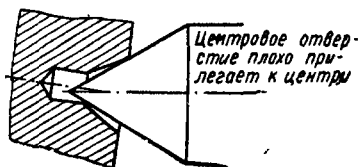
Схема контакта центрового отверстия и центра при смещении корпуса задней бабки.
